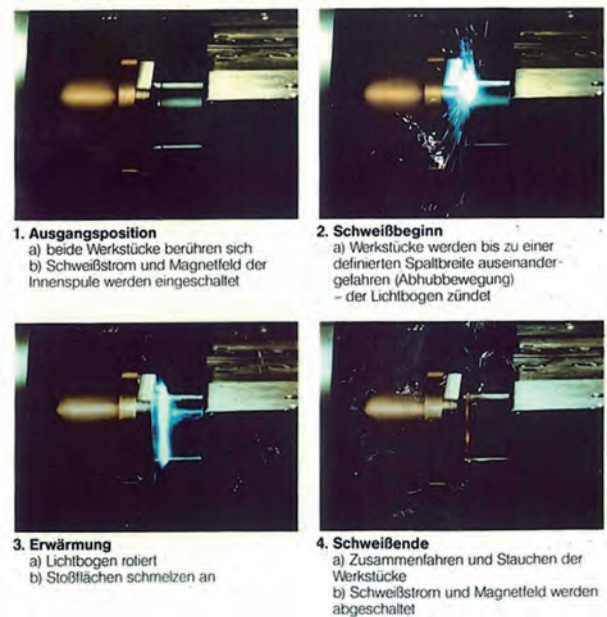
Das MagnetArc – Schweißverfahren (Quelle: KUKA Augsburg)
